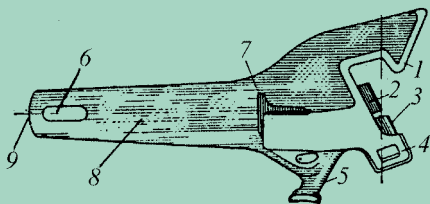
Автосцепка СА-3 (устройство корпуса автосцепки)
